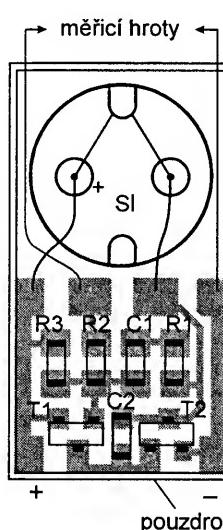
Deska s plošnými spoji zkoušečky zkratů
